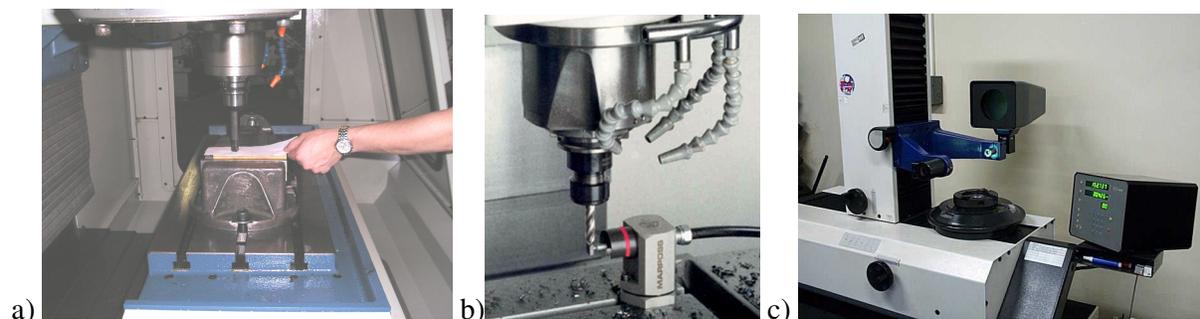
Técnicas para medir ferramentas para máquinas CNC
